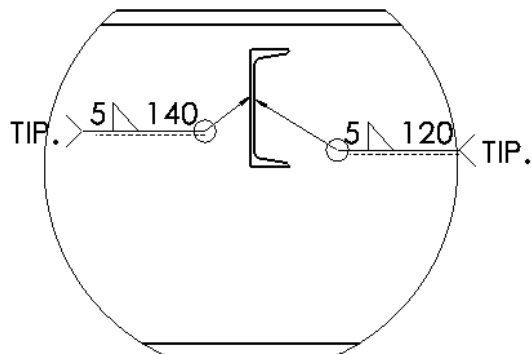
Soldadura de Viga Principal y Travesaños
